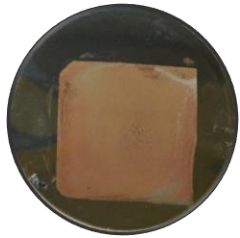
Im Werkzeug fixierte Edelstahlrunde, welche im Vorfeld auf einer standalone Tampondruckanlage bedruckt wurde.
